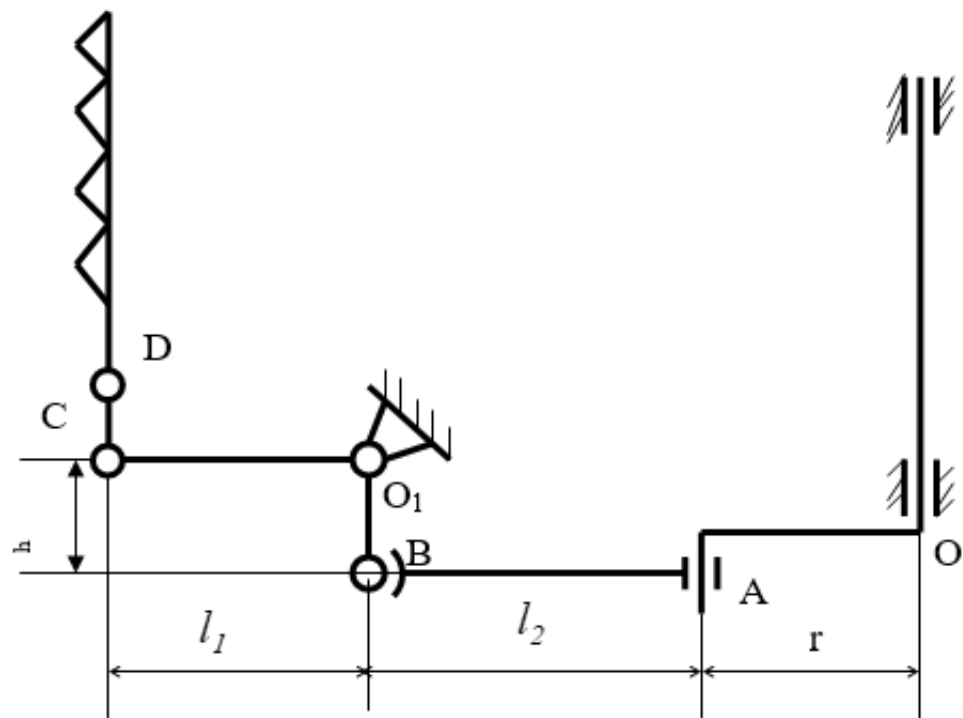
Кінематична схема механізму привода ножа модернізованої жатки.
